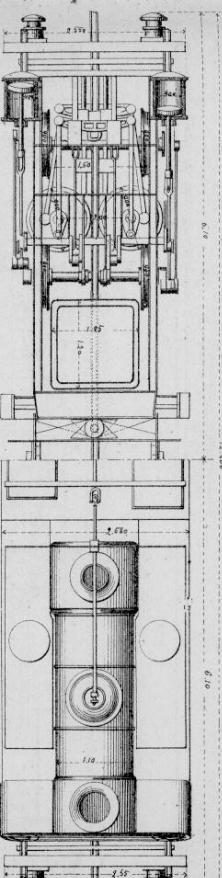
Plan, coupe horizontale à 0.021 p.m.
